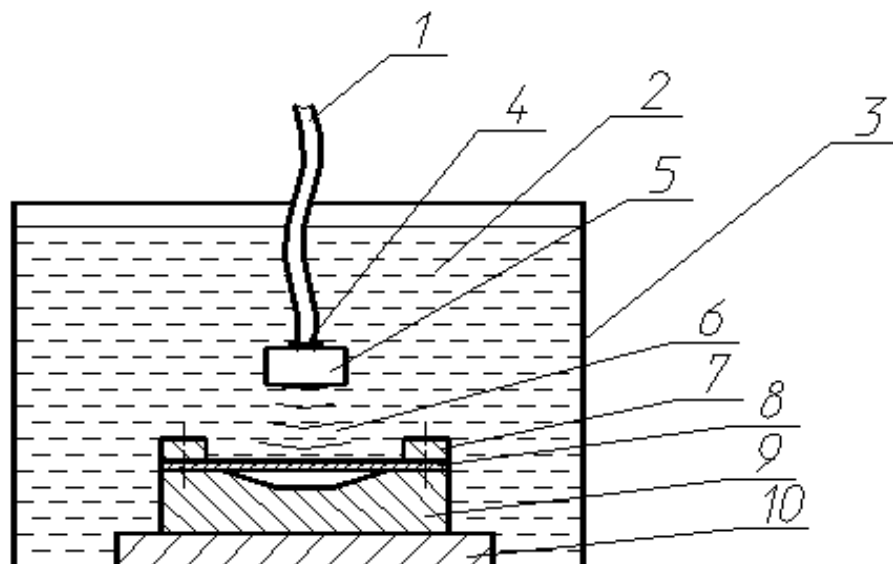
Штампування вибухом: 1 – провід, 2 – вода, 3 – бак, 4 – детонатор, 5 – запал, 6 – вибухова хвиля, 7 – притискачі, 8 – заготовка, 9 – матриця, 10 – основа
